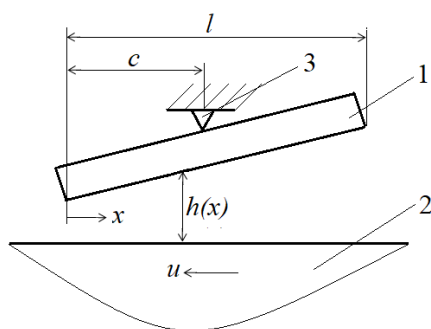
Схема упорного подшипника скольжения с самоустанавливающейся подушкой.
